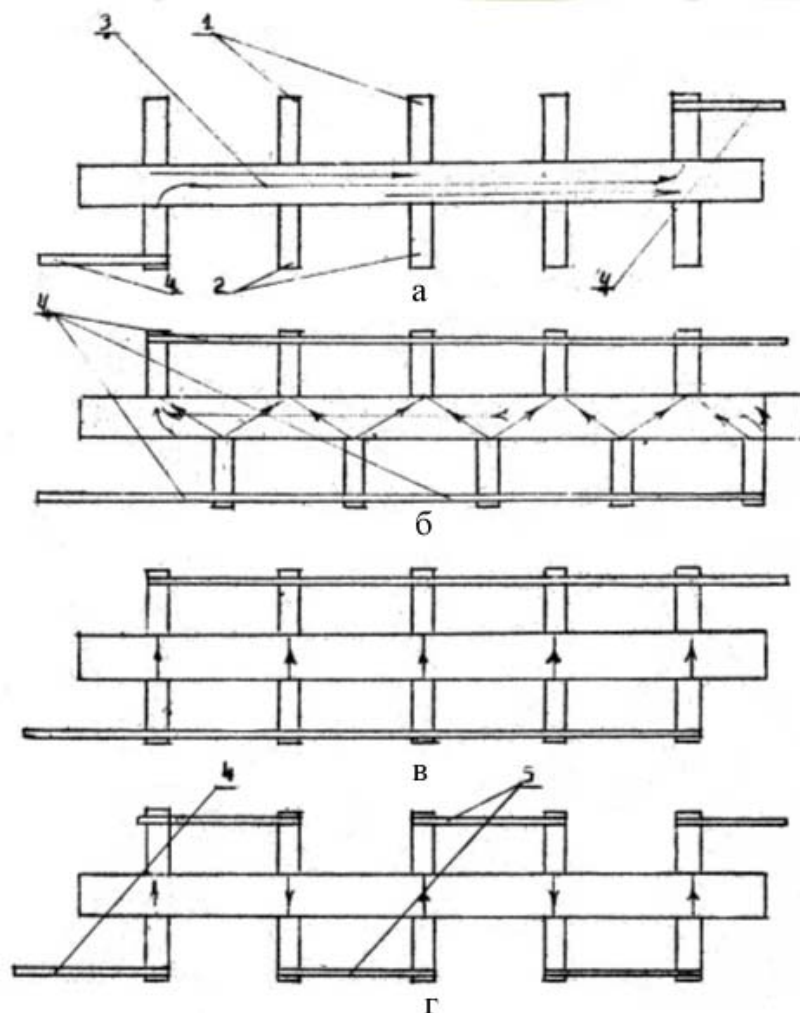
Схемы включения заготовки для контактного нагрева
